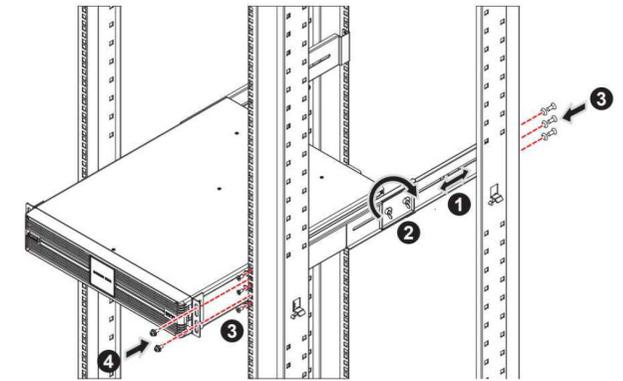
Установка внешнего батарейного блока Delta в стойку
